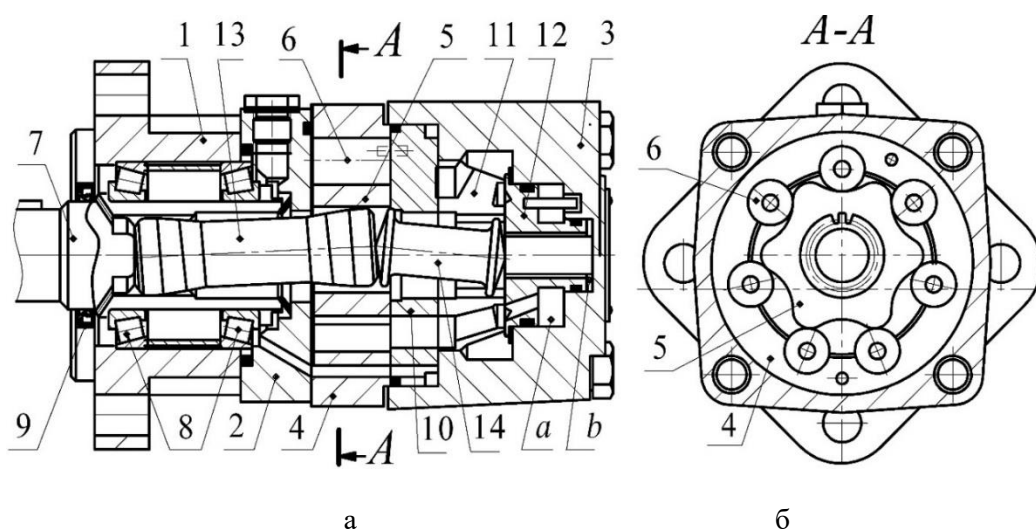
Героторный гидромотор: а – продольный; б – поперечный разрезы
